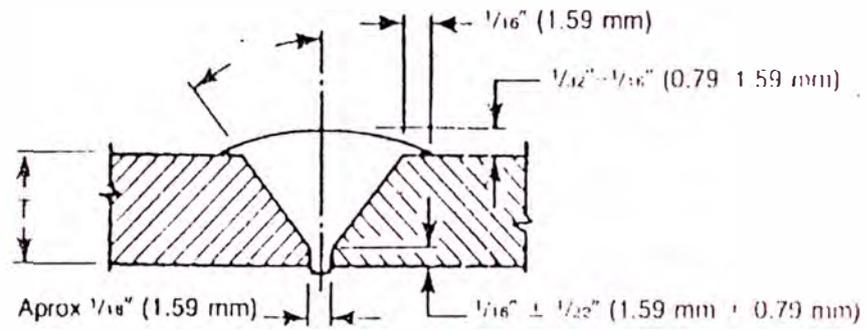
Diseño de junta de reparación para soldadura a tope con bisel en V
